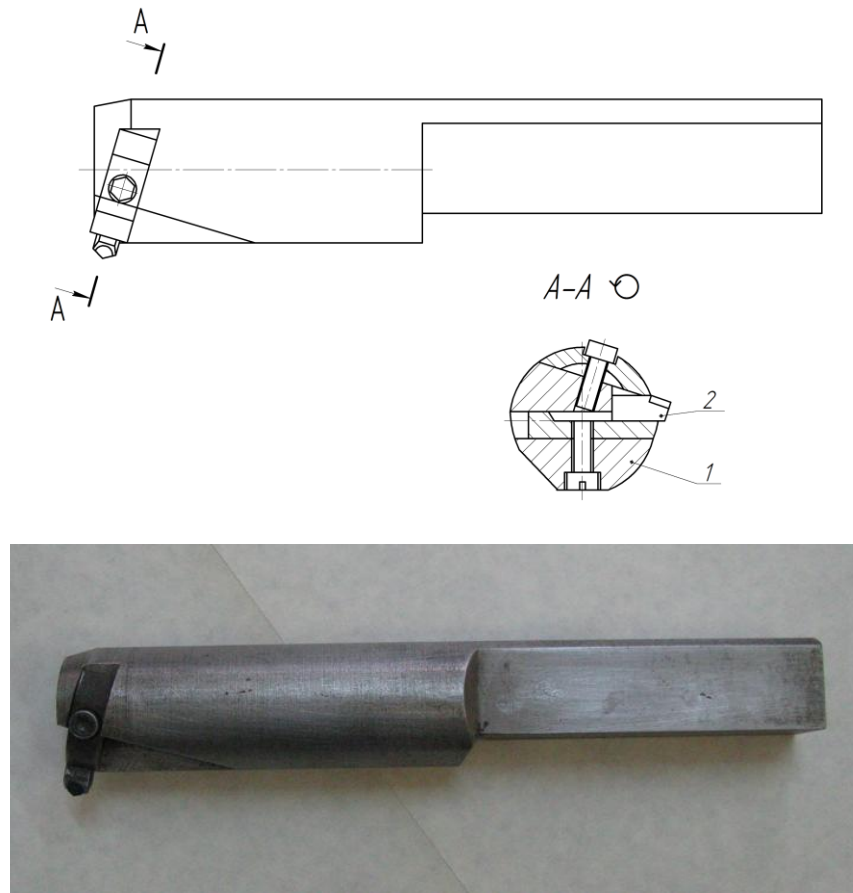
Конструкция и общий вид расточного резца с механическим креплением универсальной резцовой вставки: 1 – державка; 2 – резцовая вставка
